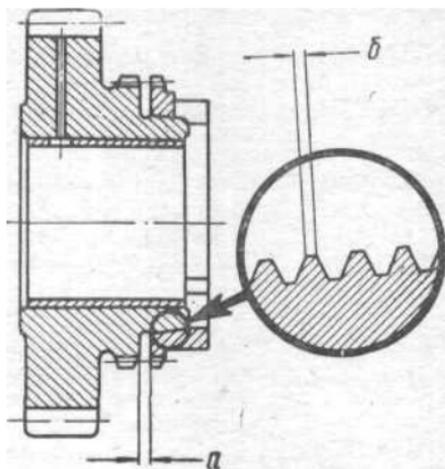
Установка блокирующего кольца синхронизатора на конусе шестерни
